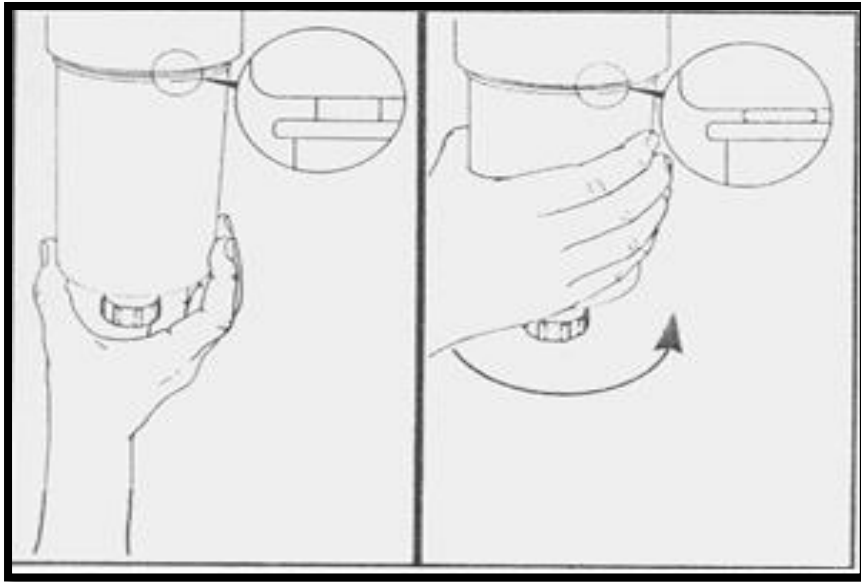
Montaje del filtro de aceite. Fuente: Manual de operación, planta Cummins
